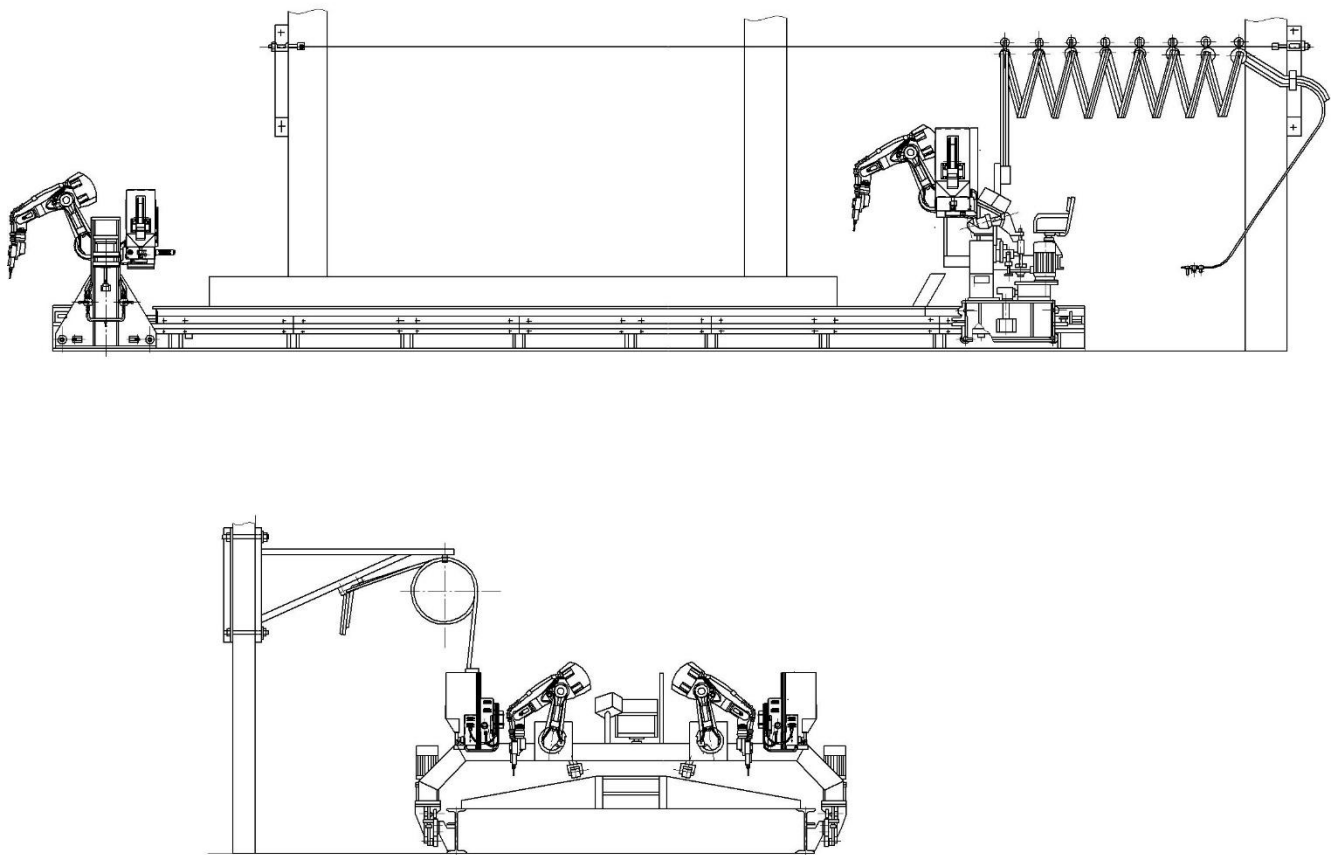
Схема модернізованої складально-зварювальної установки для виготовлення даху вагона
